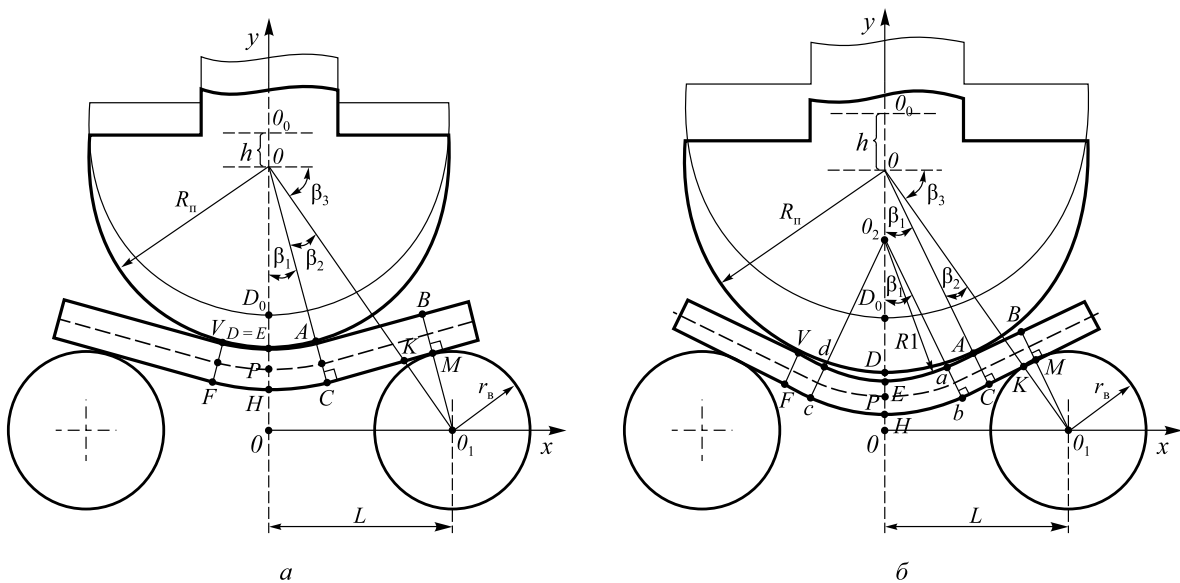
Схема очага деформации при изгибе: *а* – полный контакт заготовки с гибочным валком; *б* – отрыв заготовки от гибочного вала
